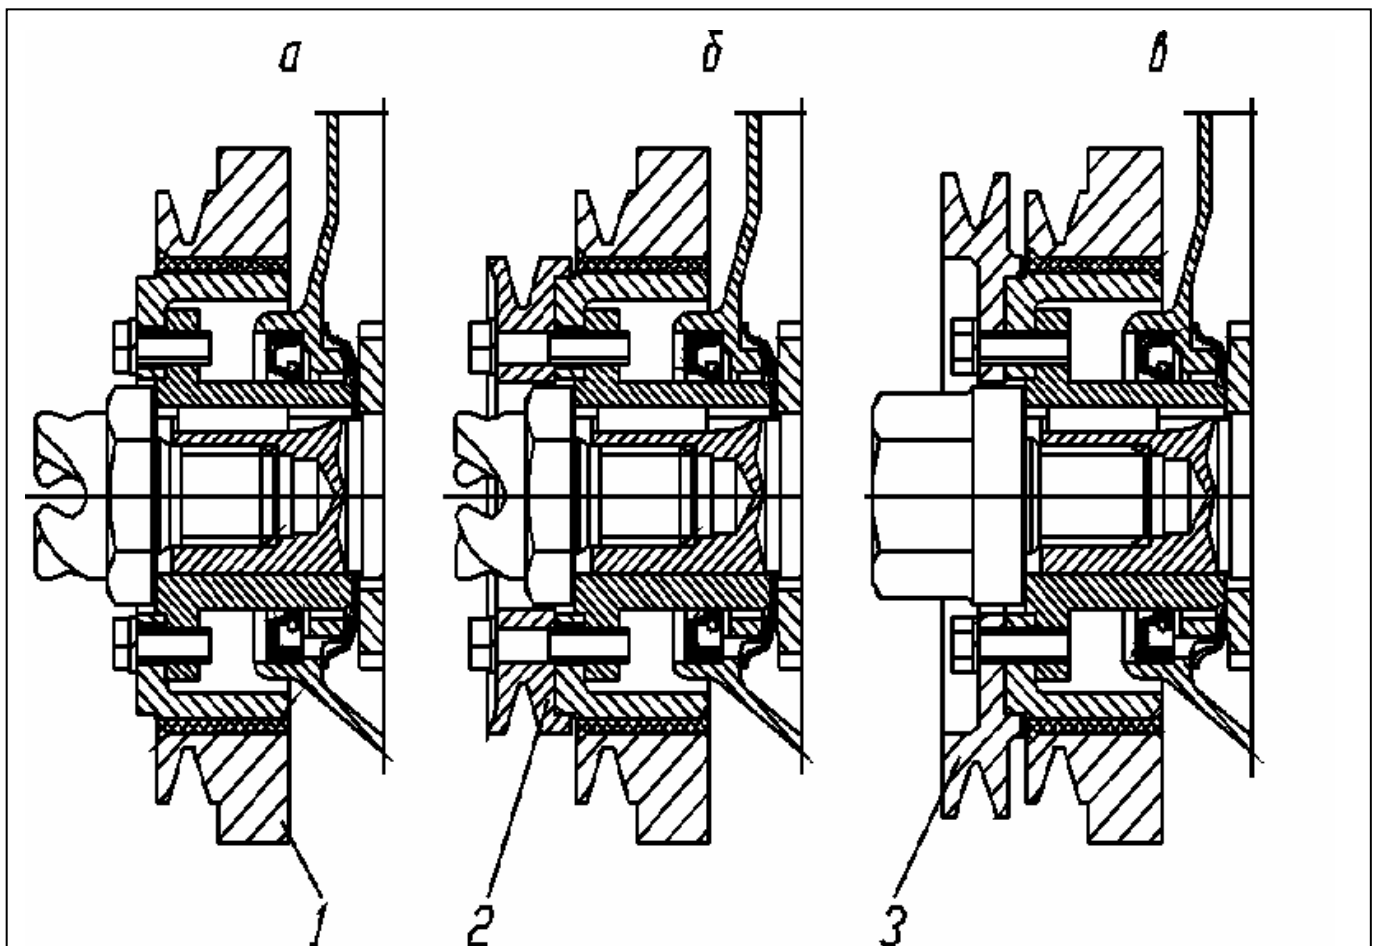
Варианты установки шкивов привода на переднем конце коленчатого вала.
